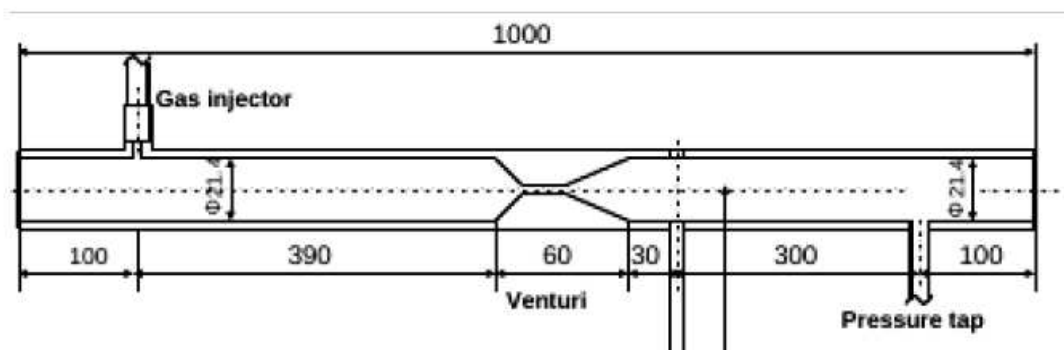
Géométrie du tube Venturi horizontal
